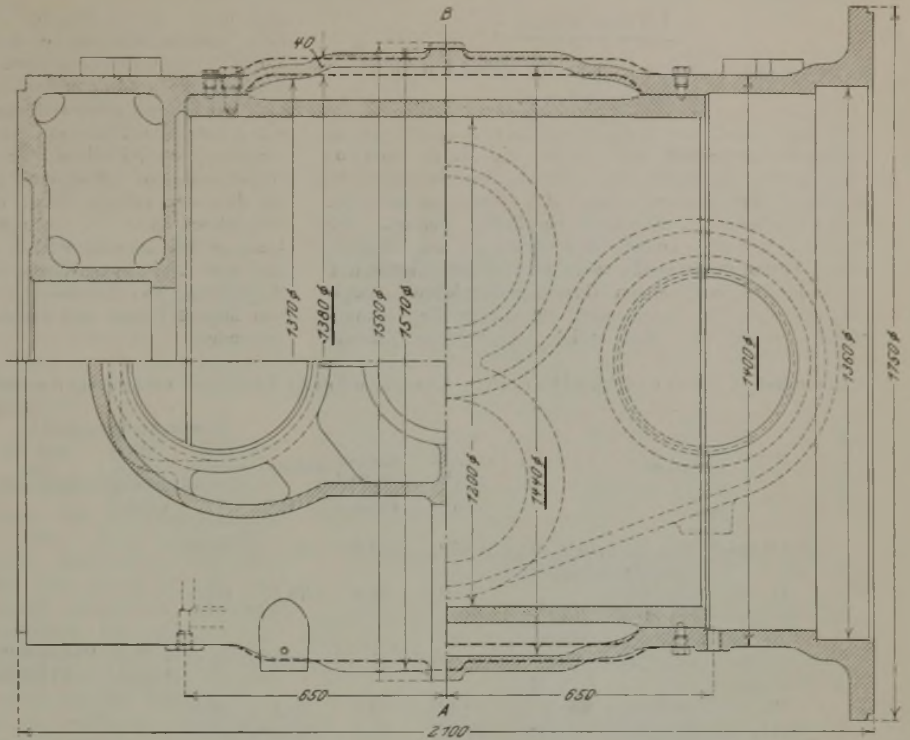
Mitteldruck-Dampfzylinder für Luftkompressoren.
